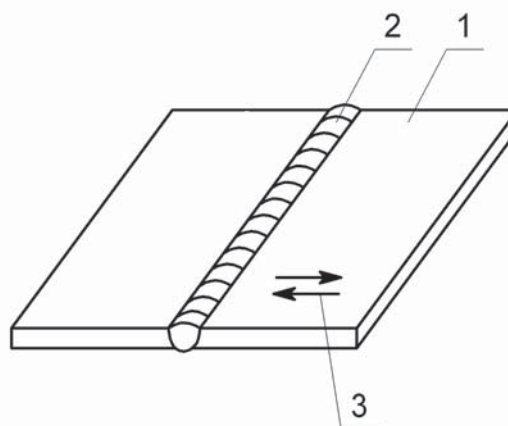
Схема сварки образцов: 1 – свариваемые пластины, 2 – сварочный шов, 3 – направления упругих колебаний
